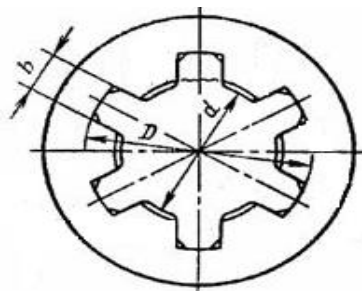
Основные геометрические размеры прямобочного шлицевого соединения
